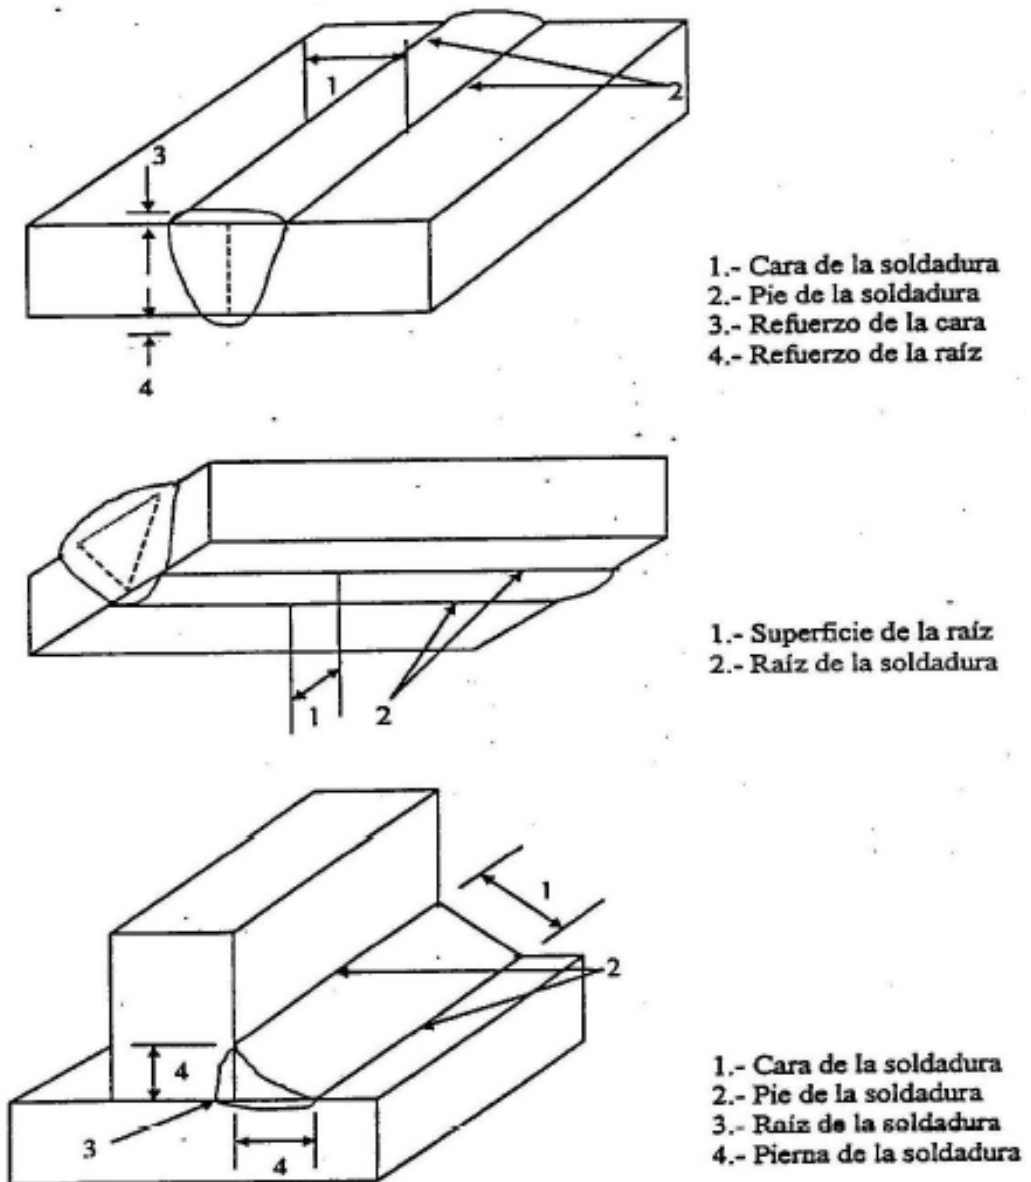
PARTES DE LAS JUNTAS SOLDADAS (Ref. 5)
